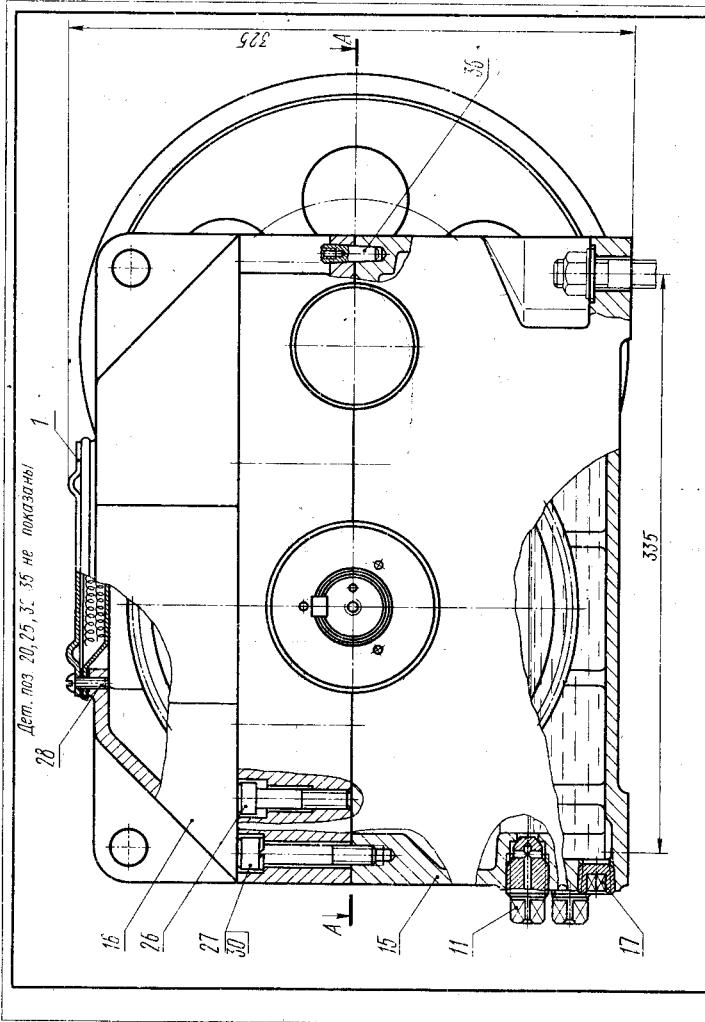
Пример сборочного чертежа цилиндрического одноступенчатого редуктора
